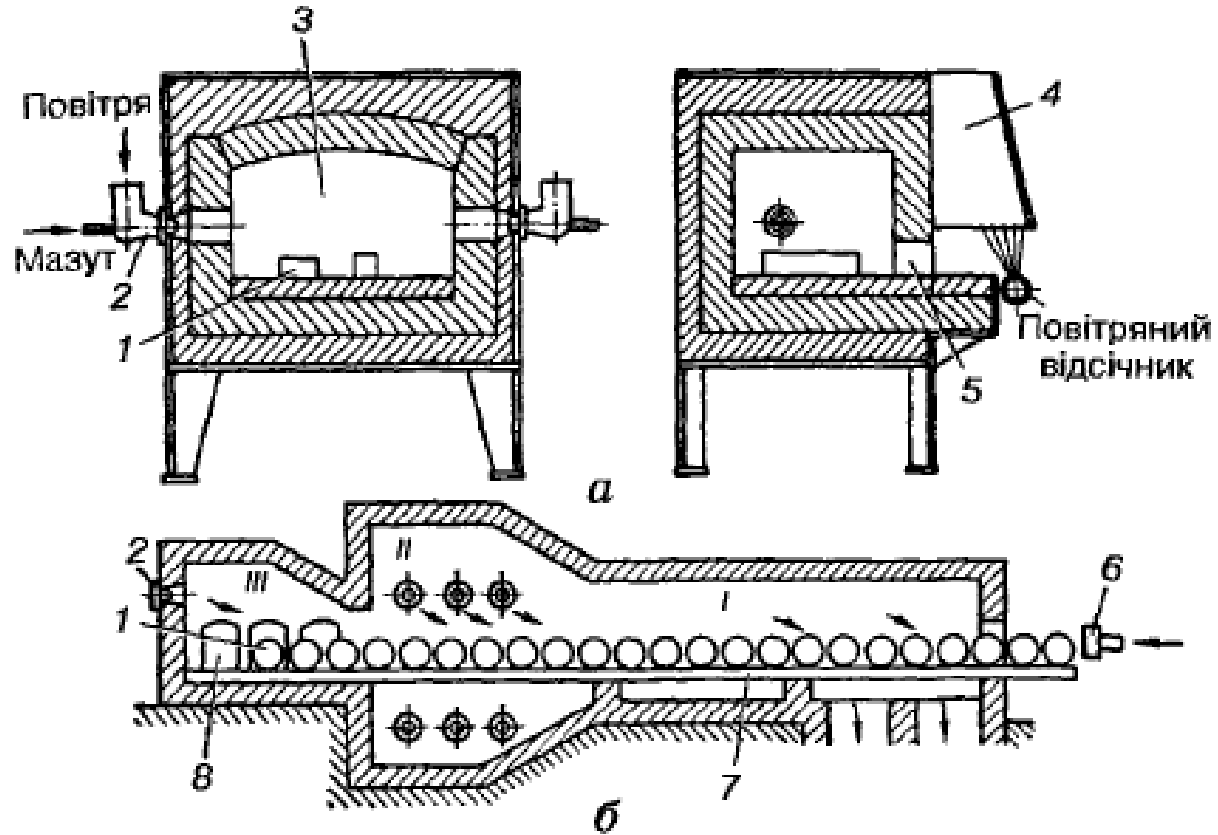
Полуменеві печі для нагрівання заготовок
